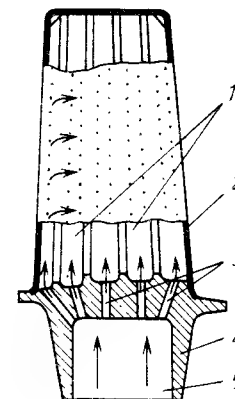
Конструктивная схема лопатки с пористым (проникающим) охлаждением
